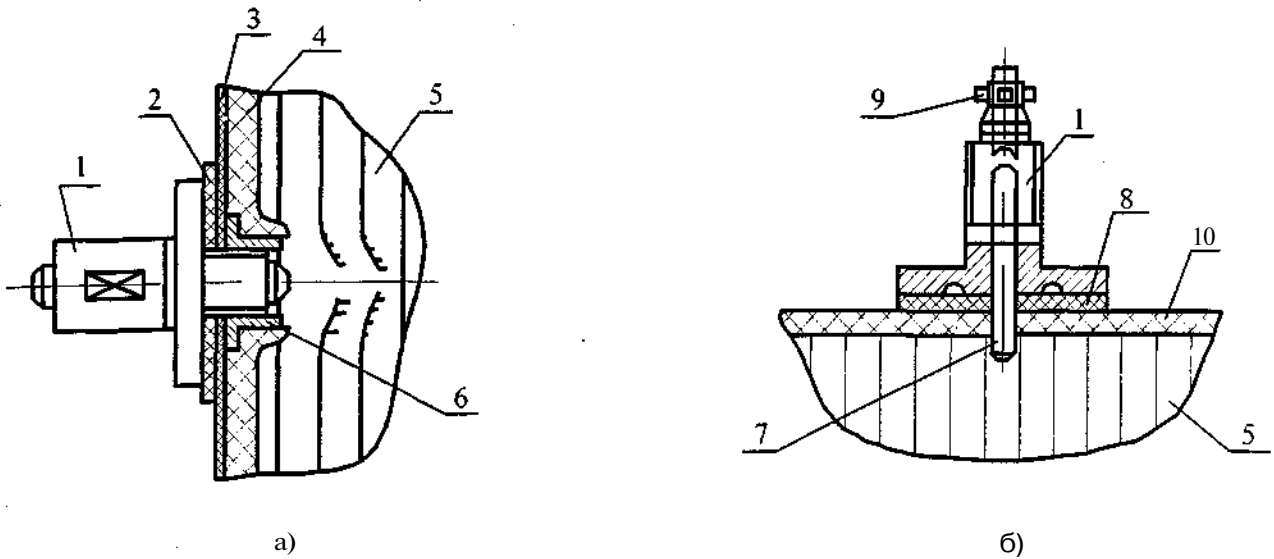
Установка штуцеров в детали каркаса и обшивку для удаления влаги : а) в каркас агрегата; б) в обшивку
